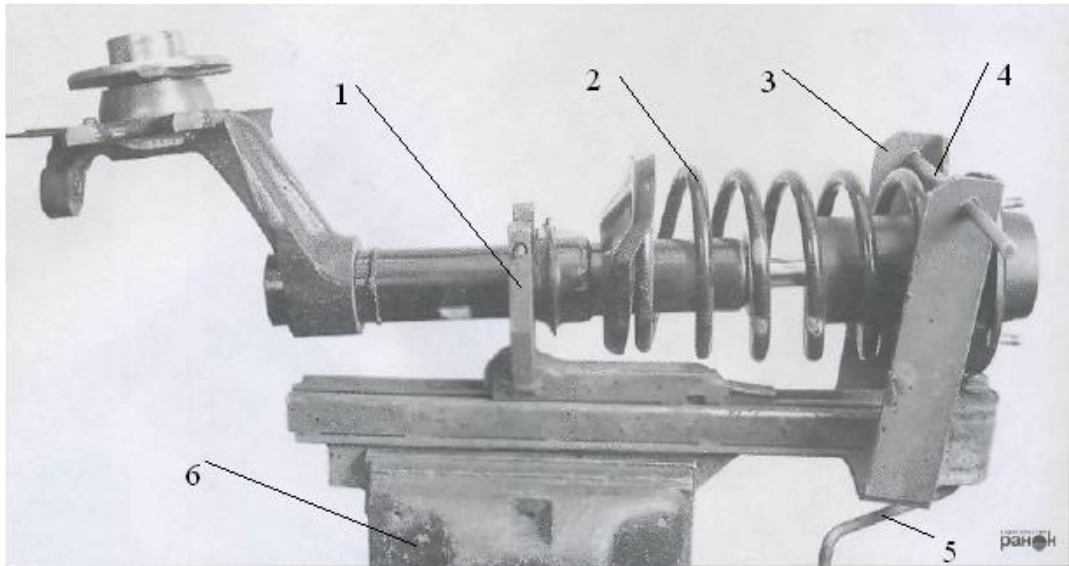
Загальний вигляд пристосування для розбирання стійки передньої підвіски автомобіля: 1 - нижня опора; 2 - пружина; 3 - верхня опора; 4 - стопорний штир; 5 - рукоятка; 6 – лещата.
